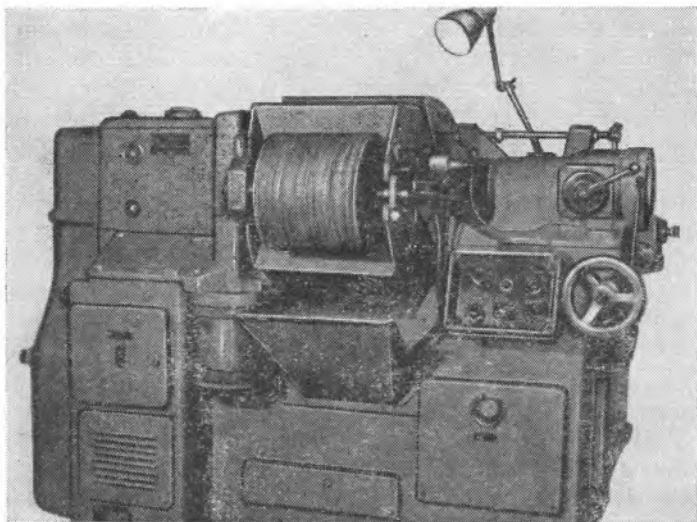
Токарный операционный станок КТ-80а для обработки периферии шлифовальных кругов диаметром 100—300 мм
